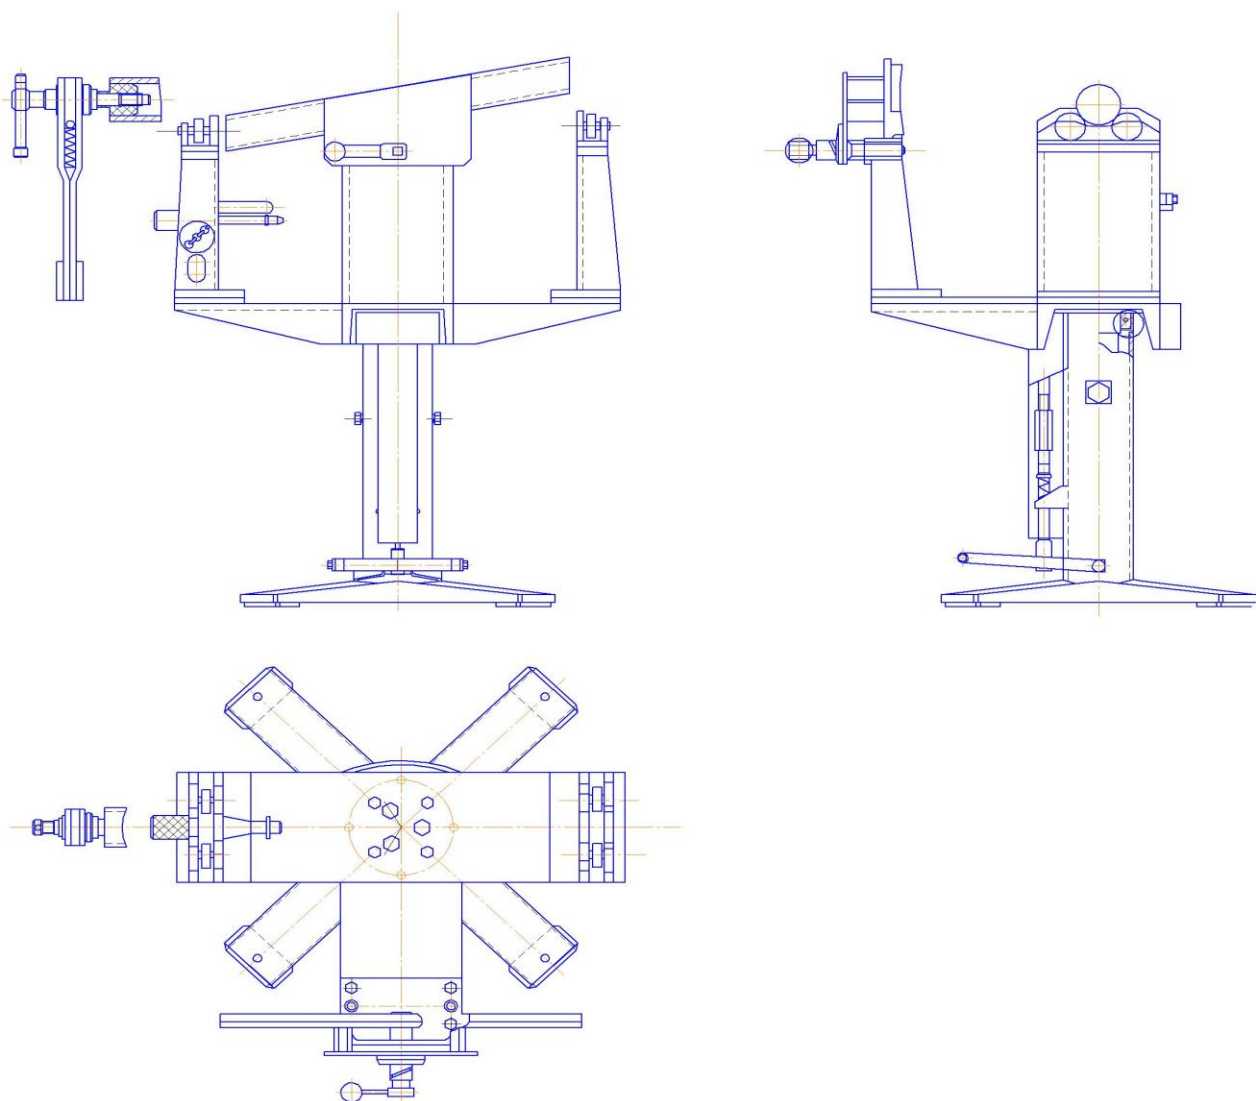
Стенд-кантователь для разборки и сборки измельчающего барабана КСК-100
